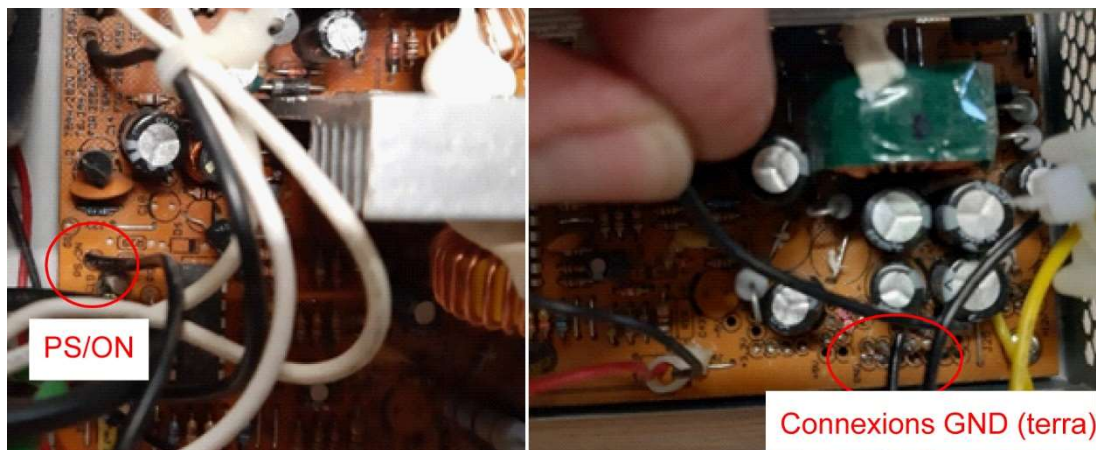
Unió pins PS/ON i GND amb un cable, soldant els extrems.
